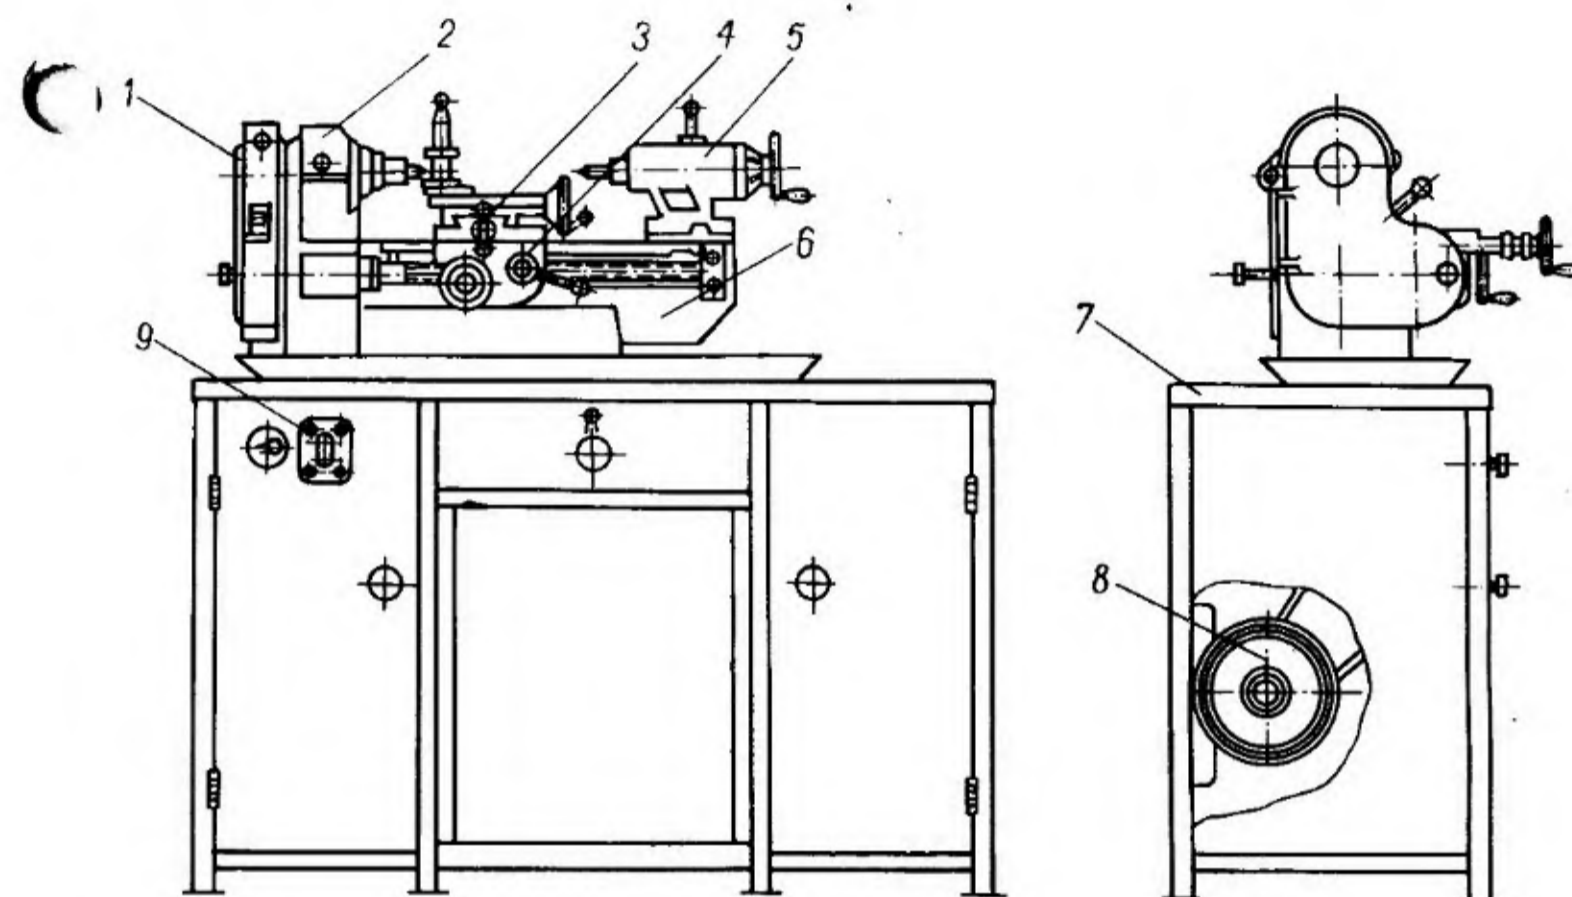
Общий вид токарно-винторезного станка модели ТВ16-III:
